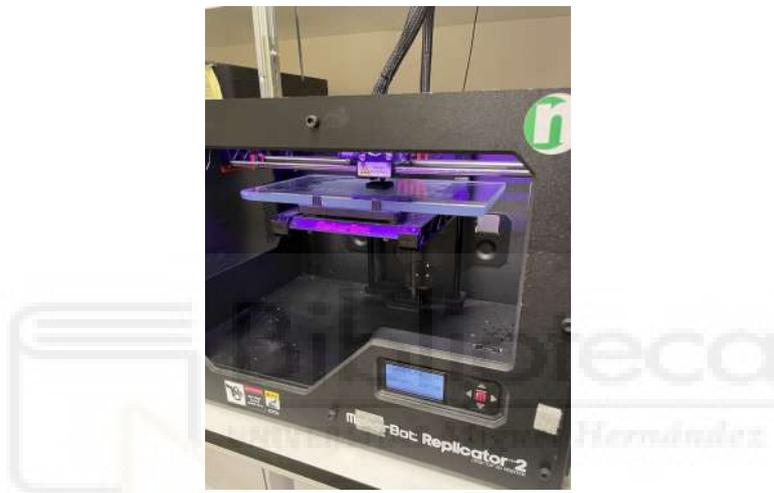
Impresora 3D MakerBot imprimiendo una pieza
